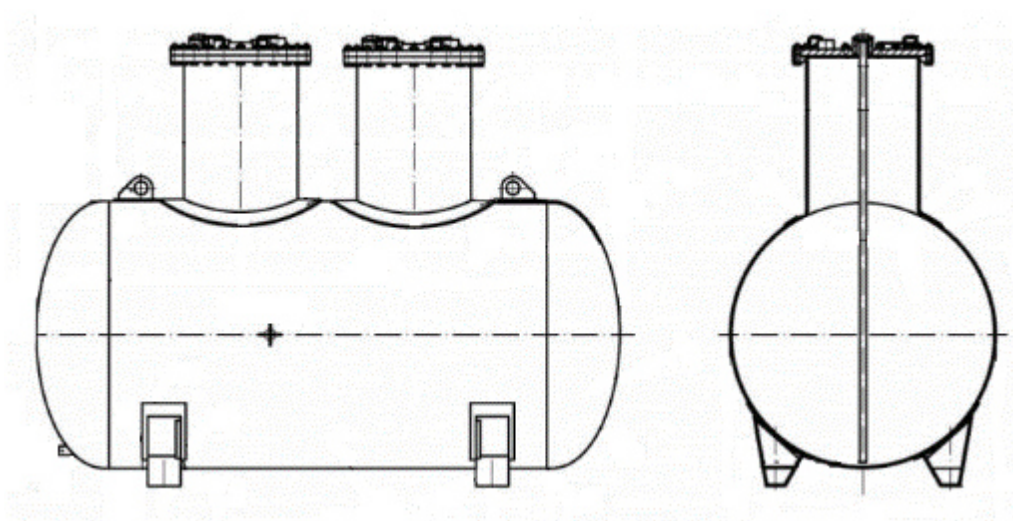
Эскиз общего вида резервуаров РГС-50
